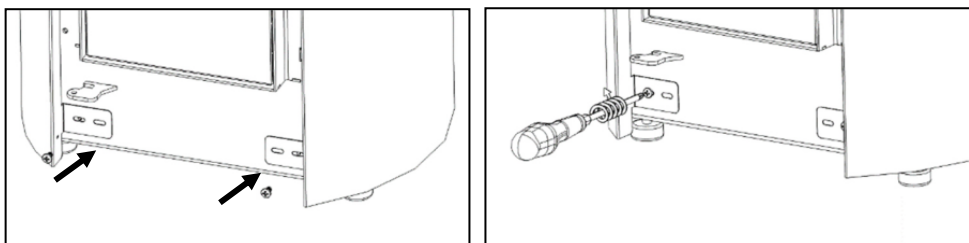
Fijación de la tapa en la parte frontal del equipo
